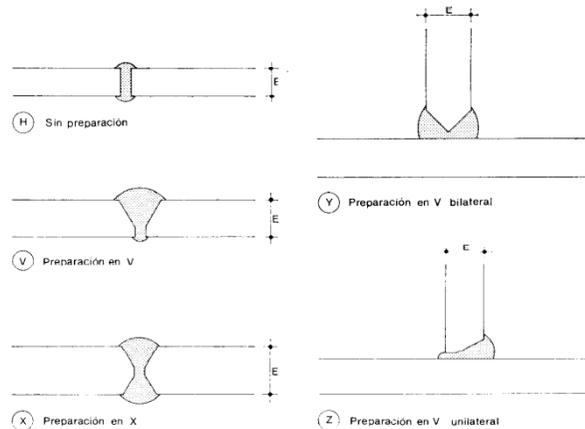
y fotografía 13b: Soldadura a tope.
